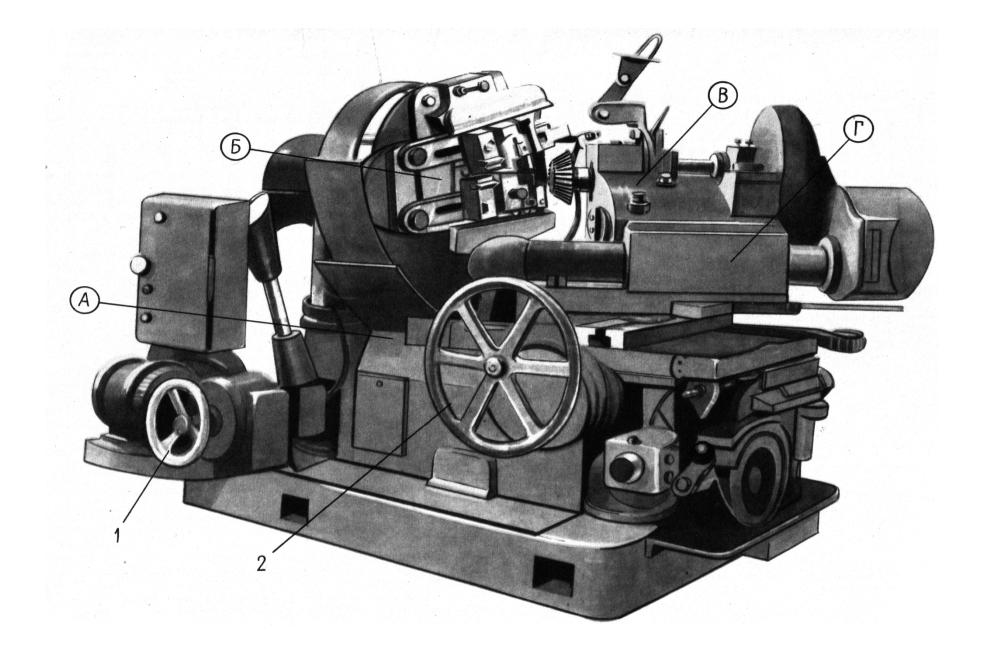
Общий вид зубострогального станка для конических колёс модели 526
